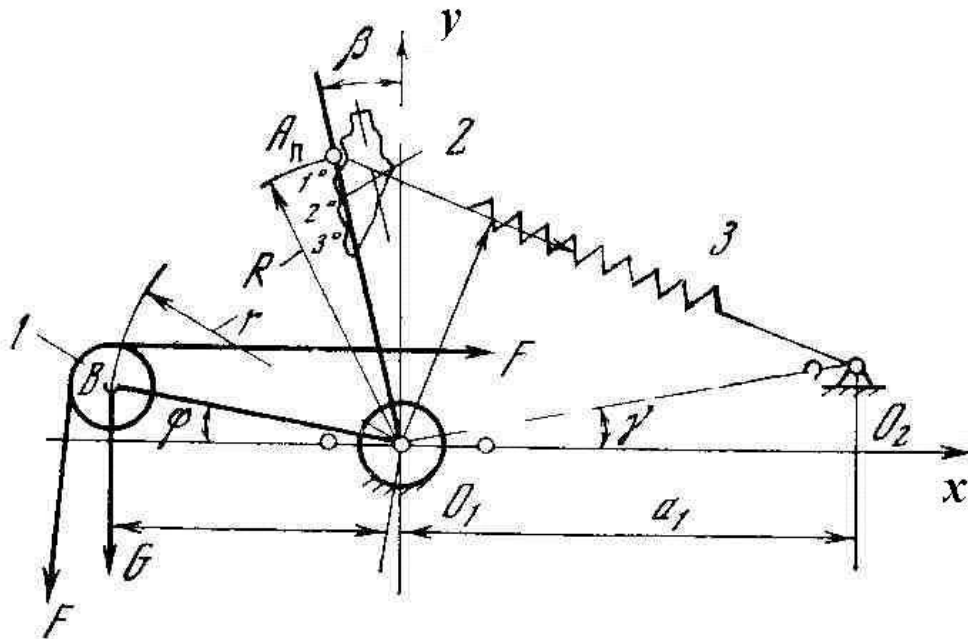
Розрахункова схема механізму хитного скала верстата СТБ
